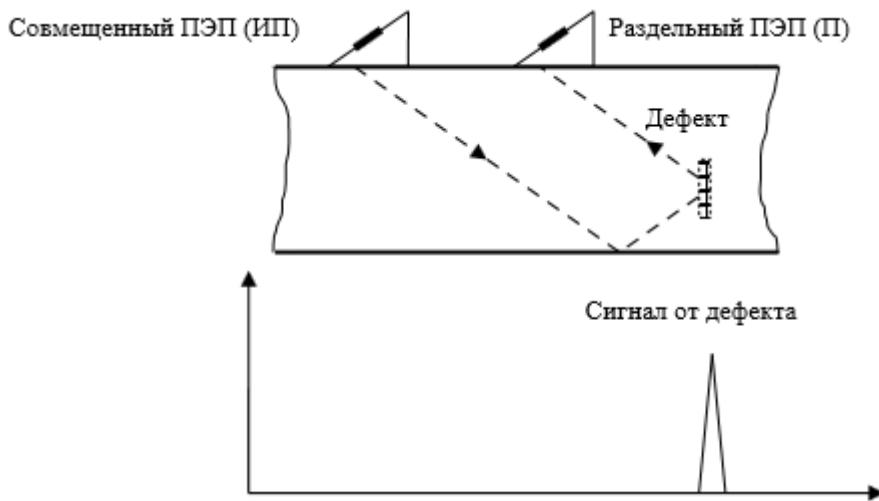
Схема прозвучивания и А – развертка зеркального метода
